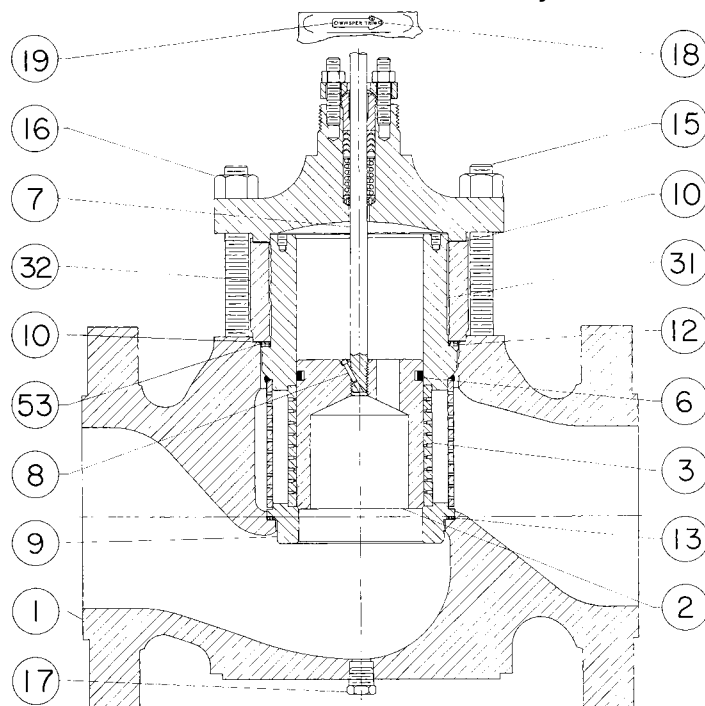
Стандартные клапаны конструкции ED и EAD Fisher размером 1 - 6
